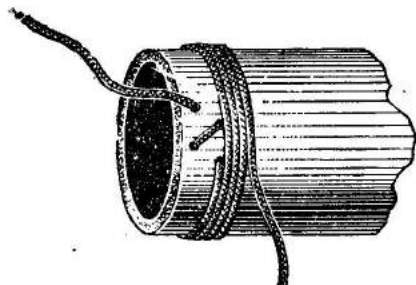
, I. Крепление конца у однослойной цилиндрической катушки.
